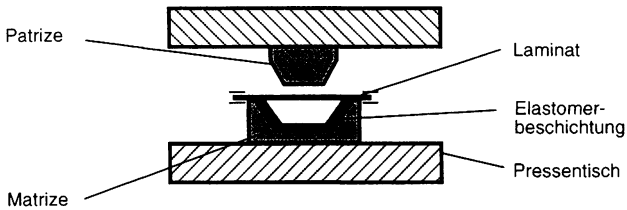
Stempelumformen mit beschichtetem Unterwerkzeug („Shaped Rubber Tool“)
